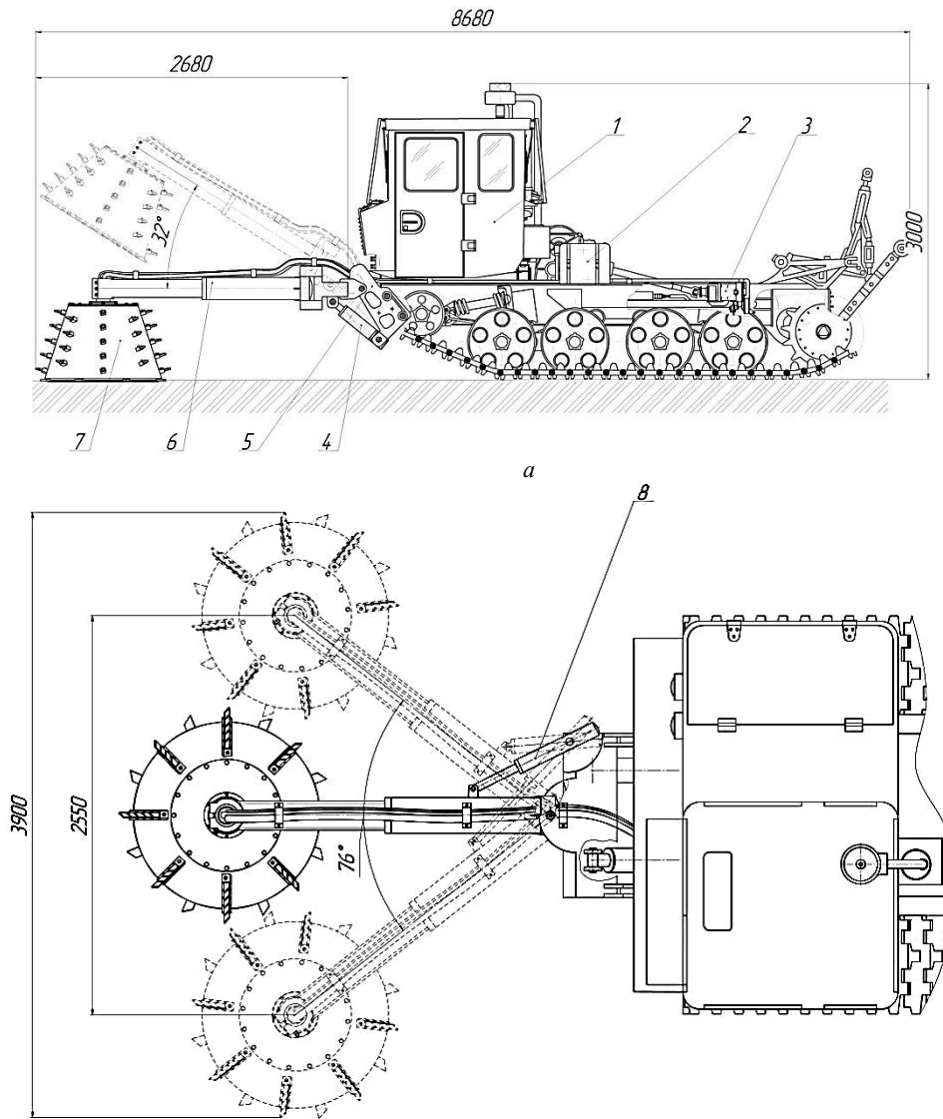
Общий вид проектного орудия: *а* – вид сбоку, *б* – вид сверху; 1 – базовый трактор; 2 – бак масляный; 3 – гидронасос; 4, 8 – гидроцилиндры; 5 – навеска; 6 – стрела; 7 – фреза
